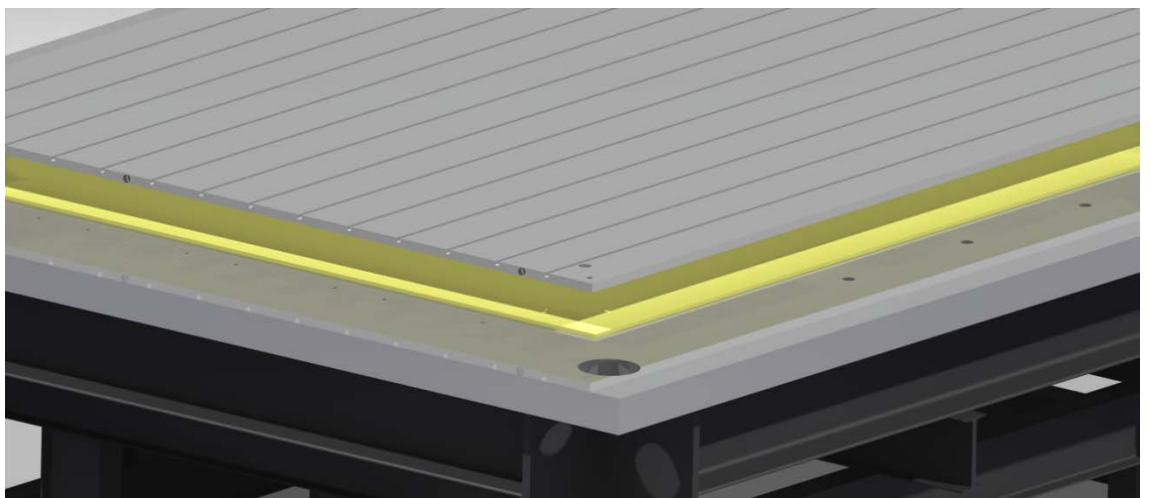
Ejemplo de la colocación de plancha BARLAN 1250 entre las placas
